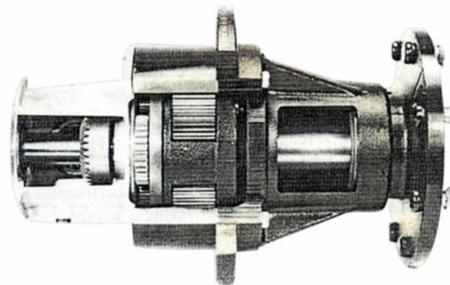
Колесный редуктор тележки ДМ «Кубань-ЛК1» с передачей планетарного типа
